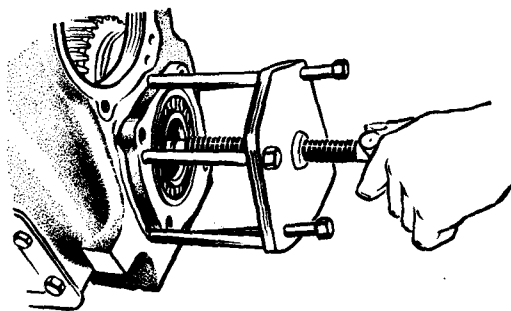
Выпрессовка стакана в сборе с задним подшипником промежуточного вала
